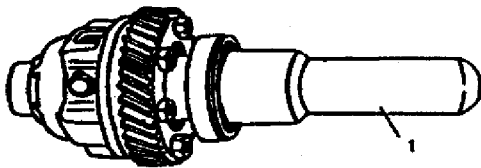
Instalação do rolamento: 1 - ferramenta 67.7853-9558
